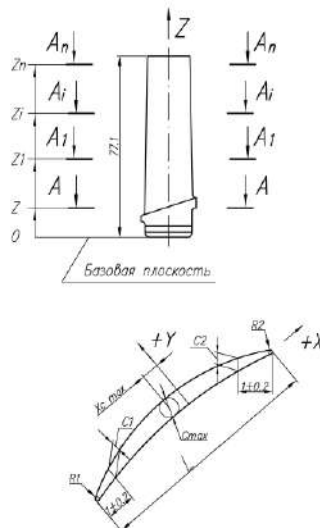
Лопатка I ступ. компресора двигуна ТВЗ-117 (схема профілю)
